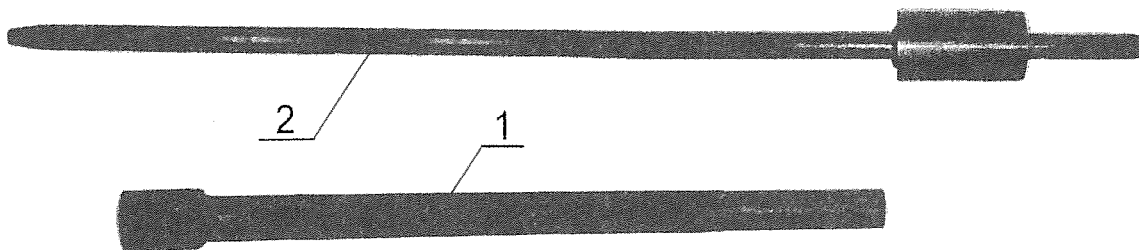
Пристрій для вибивання циліндрового механізму врізного замка СВМ-1СТ.
